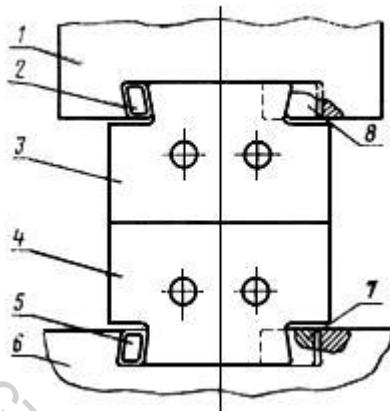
Схема крепления штампов и бойков в бабе и подушке: 1 – баба; 2 – верхний клин; 3 – верхний штамп (боек); 4 – нижний штамп (боек); 5 – нижний клин; 6 – подушка (штамподержатель); 7 – шпонка; 8 – прокладка
